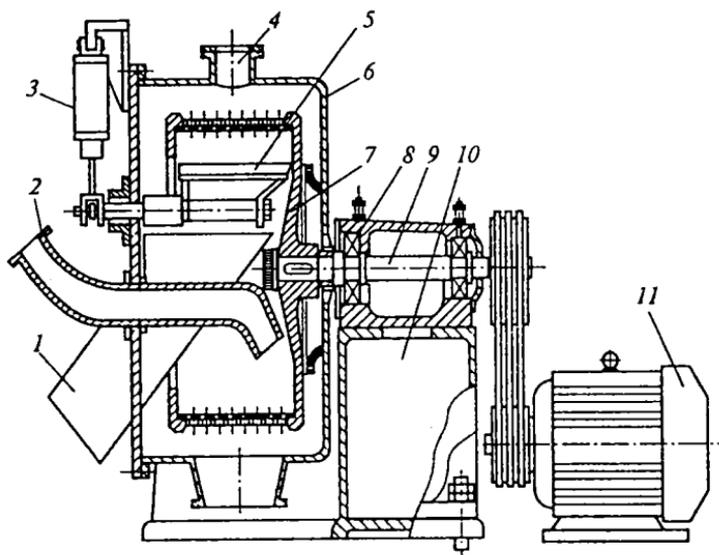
Схема горизонтальной ножевой центрифуги с автоматизированной выгрузкой осадка: 1 — бункер; 2 — труба; 3 — привод механизма среза осадка; 4 — люк-воздушник; 5 — нож; 6 — кожух; 7 — ротор; 8 — подшипник качения; 9 — вал; 10 — станина; 11 — электродвигатель
